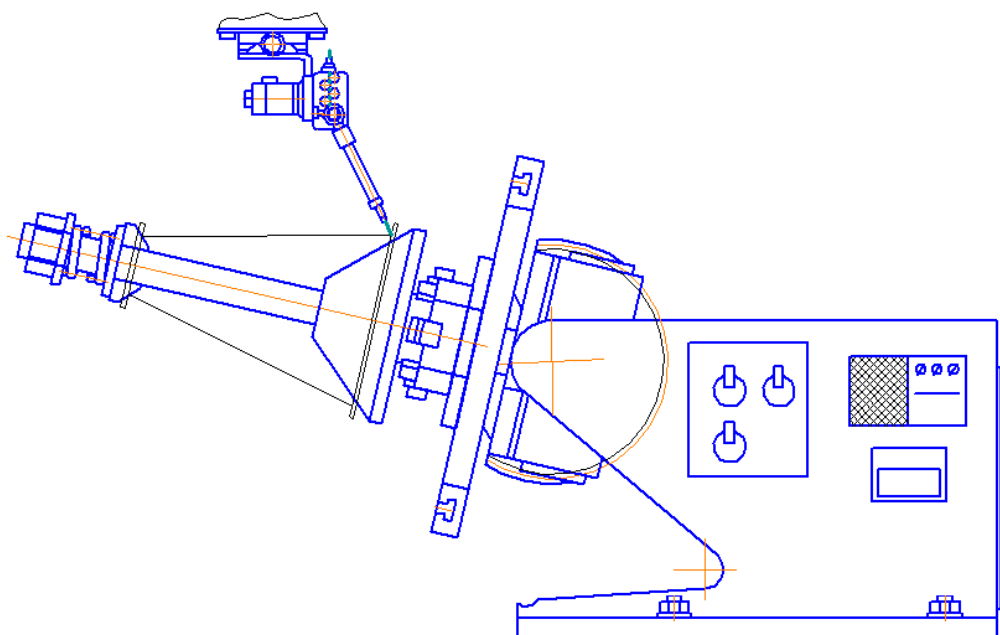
Схема налаштування обладнання для зварювання
